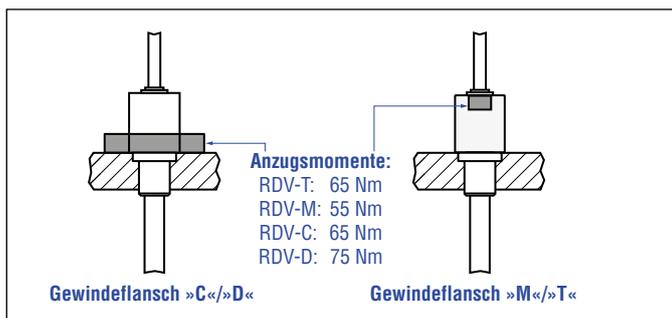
Einbaubeispiel für Gewindeflansch »C«/»D«, »M«/»T«
